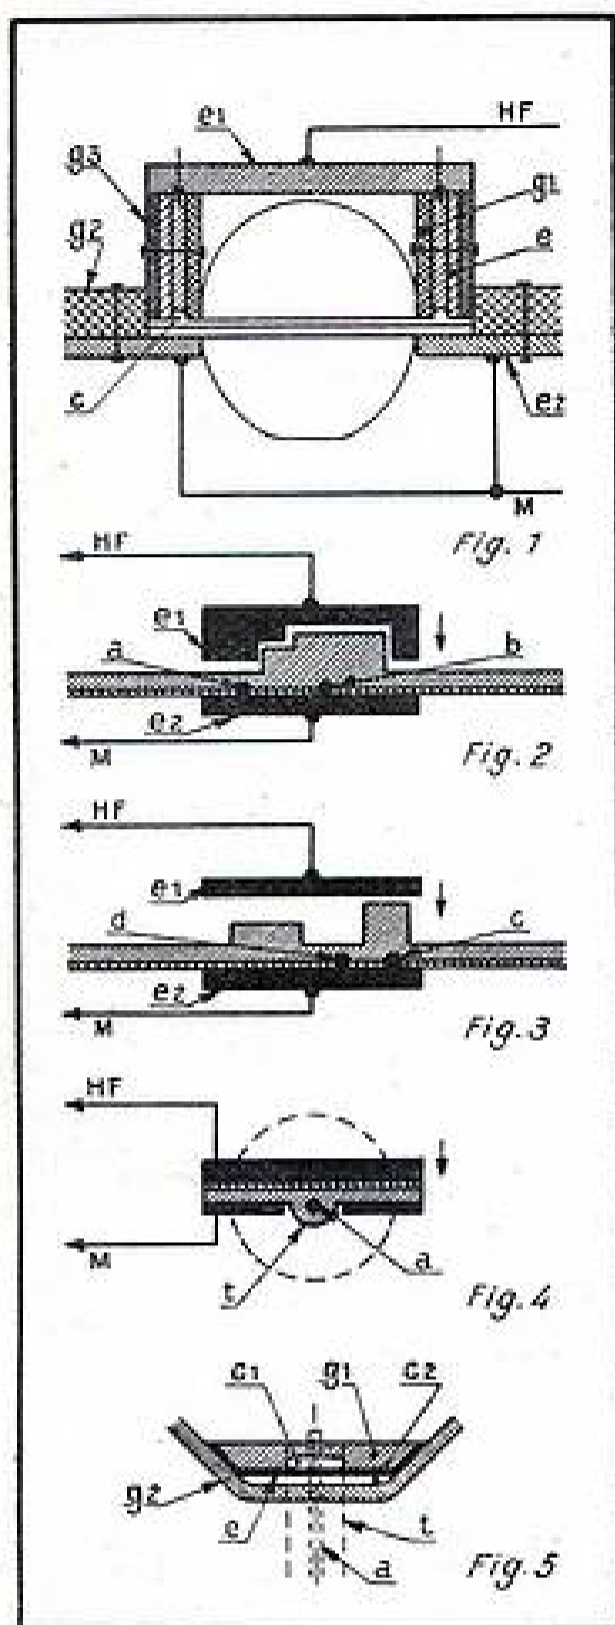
Coupe des deux électrodes destinées à la soudure des coquilles de l'ampoule auto-injectable. On remarque le sillon caractéristique du surmoulage.
